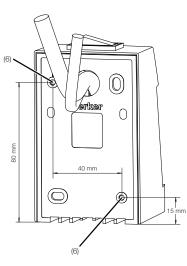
Abmessungen für rückseitige Montage des Komplettgerätes
